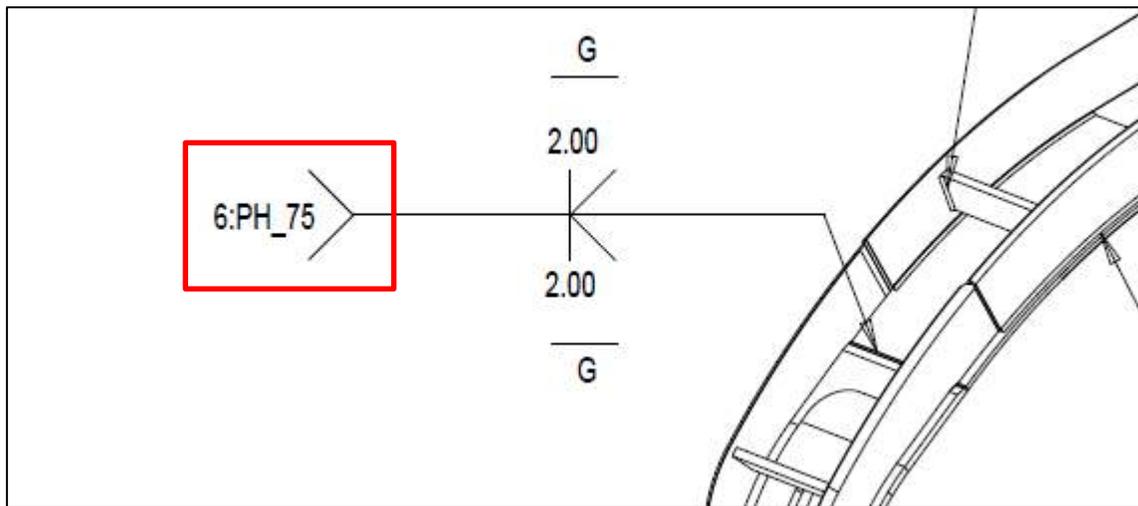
Ejemplo de Pre calentamiento en Assembly Drawing
